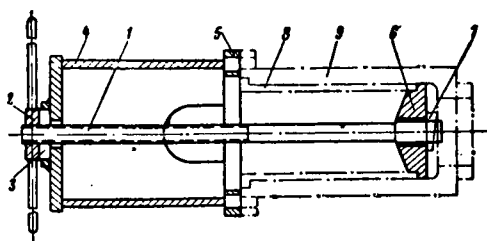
Приспособление для выпрессовки втулки цилиндра компрессора:
